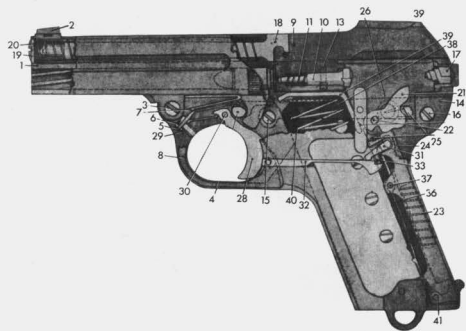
Schnittzeichnung der Pistole Modell 34 Kal. 7,65 mm.
